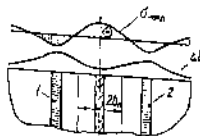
Предварительное растяжение зоны сварки местным нагревом
